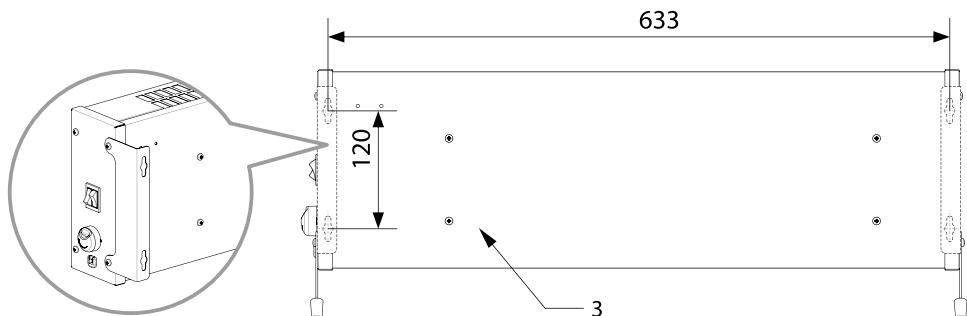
Размеры для разметки отверстий для настенного монтажа конвекторов 60-0122, 60-0123.
